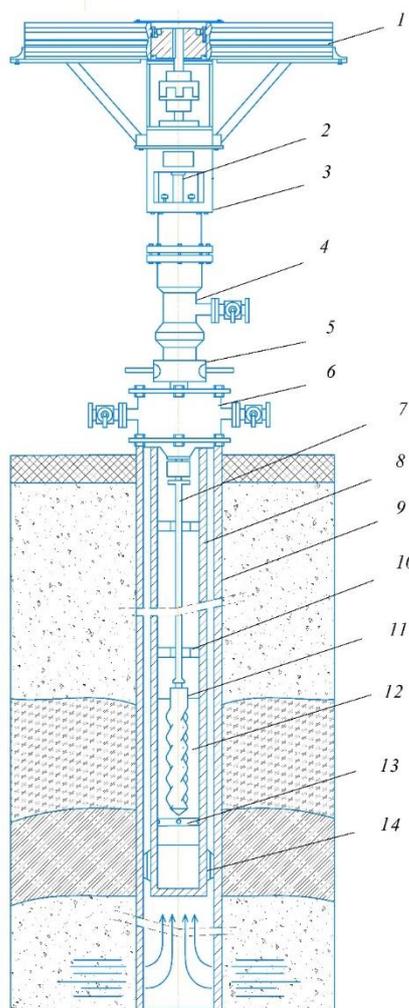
Схема установки штангового винтового насоса с изменённым приводом: 1 – двигатель СДПМ; 2 – полированный шток; 3 – приводная головка; 4 – тройник; 5 – превентор; 6 – трубная головка; 7 – штанги; 8 – насосно-компрессорные трубы; 9 – обсадные трубы; 10 – центратор; 11 – ротор (винт); 12 – статор (обойма); 13 – нижний переводник статора с упорным пальцем; 14 – динамический противоотворотный якорь (анкер).
